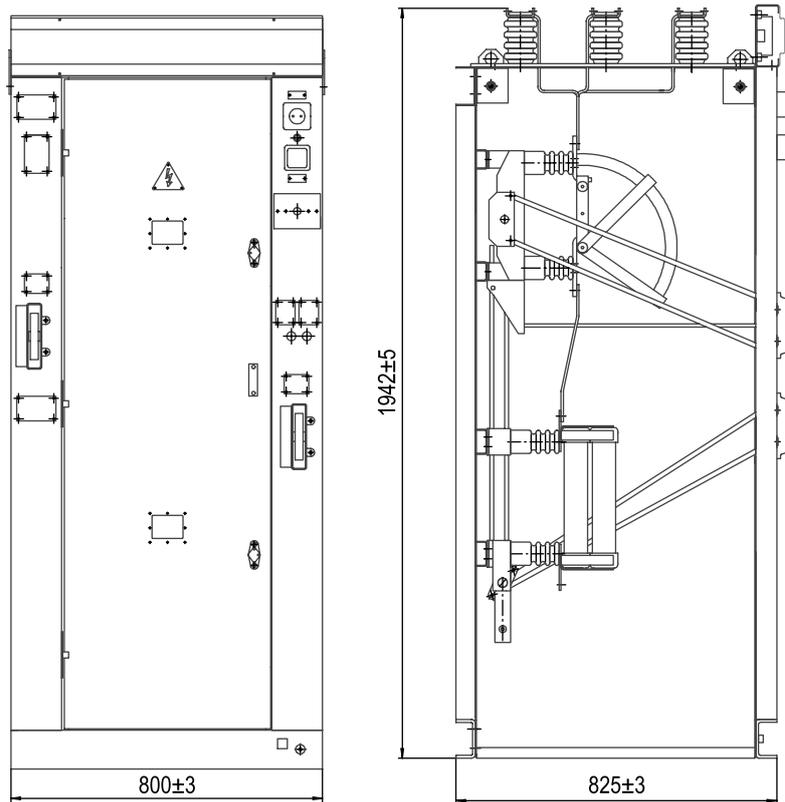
Габаритные, установочные, присоединительные размеры КСО-306 с автогазовым выключателем нагрузки ВМП-М1-10/630.
